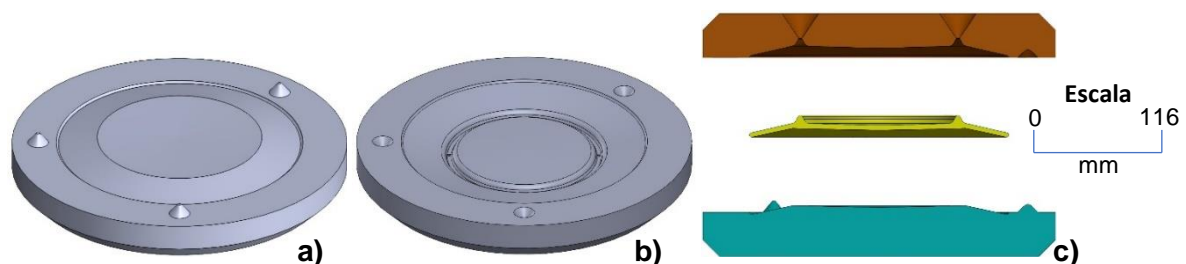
Componentes necessários para a conformação por enchimento convencional do prato do projeto: a) e b) moldes; c) montagem CAD dos moldes e do prato.
